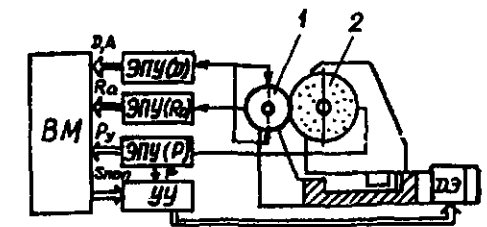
Система адаптивного управления качеством обрабатываемой детали при шлифовании: 1 – деталь; 2 – шлифовальный круг
